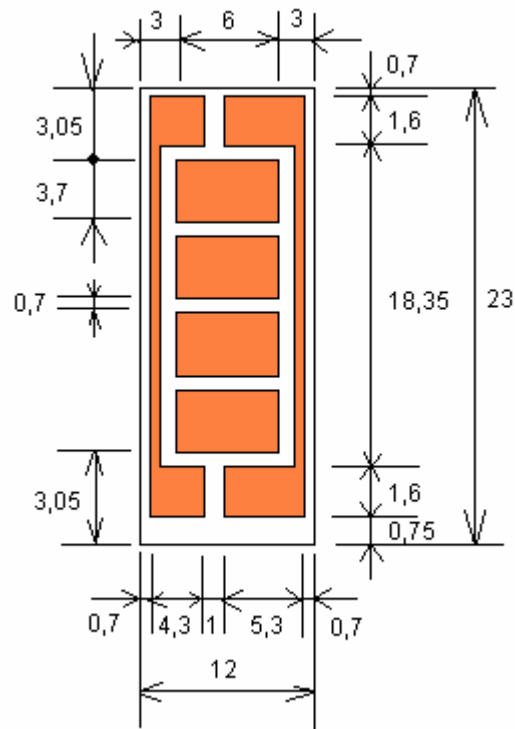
Dimensionado en mm de la parte superior del nivel 2.
